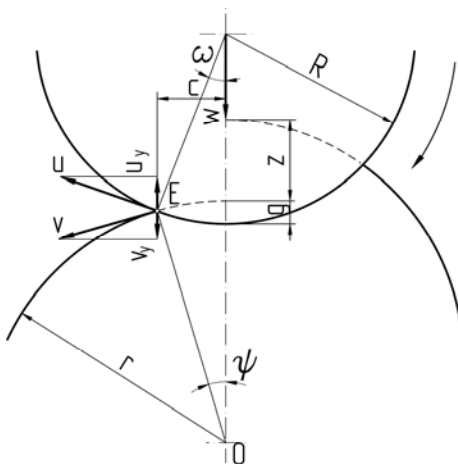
Схема к определению ширины контактной поверхности со стороны выхода заготовки из валков
